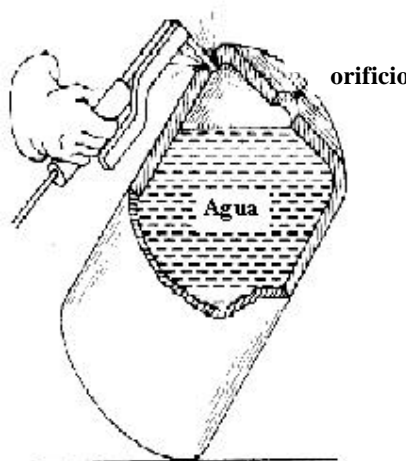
Forma segura para la soldadura de contenedores
